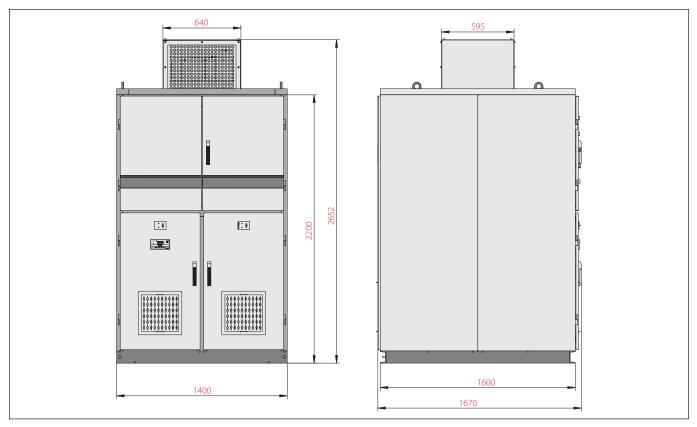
Корпус шкафа токоограничивающего реактора типоразмера ЕАО2
